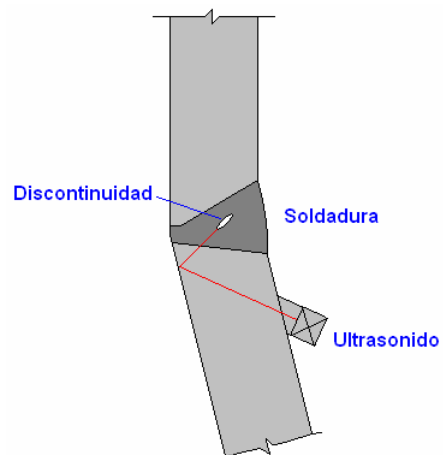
Inspección de la soldadura con ultrasonido industrial.
